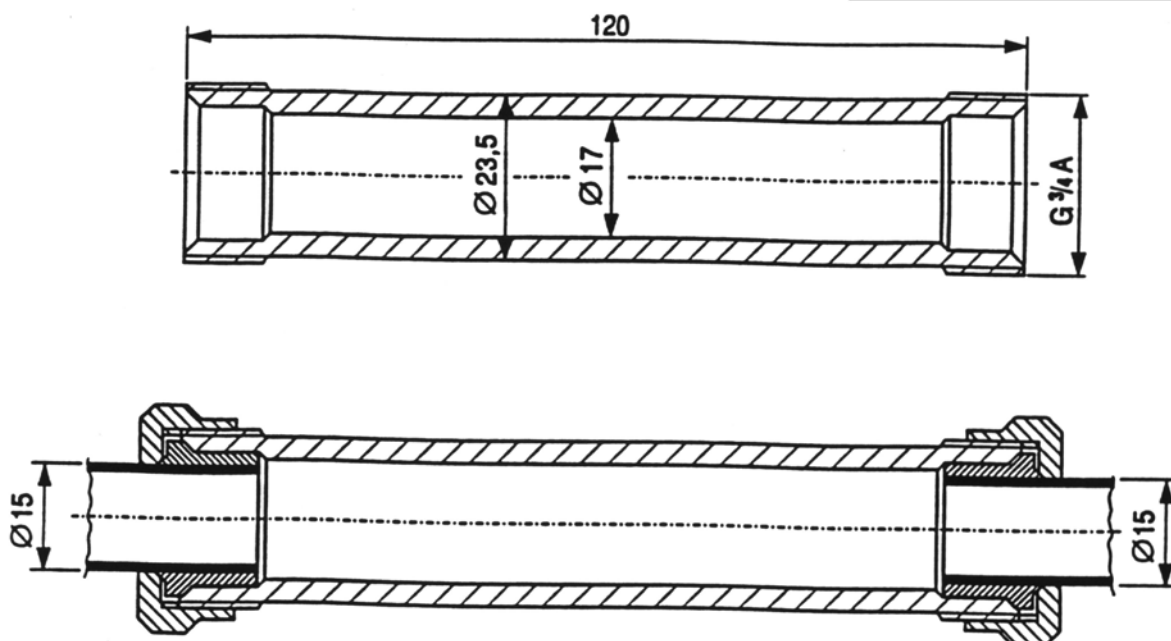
Probekörper für Versuche mit Armaturenwerkstoffen
